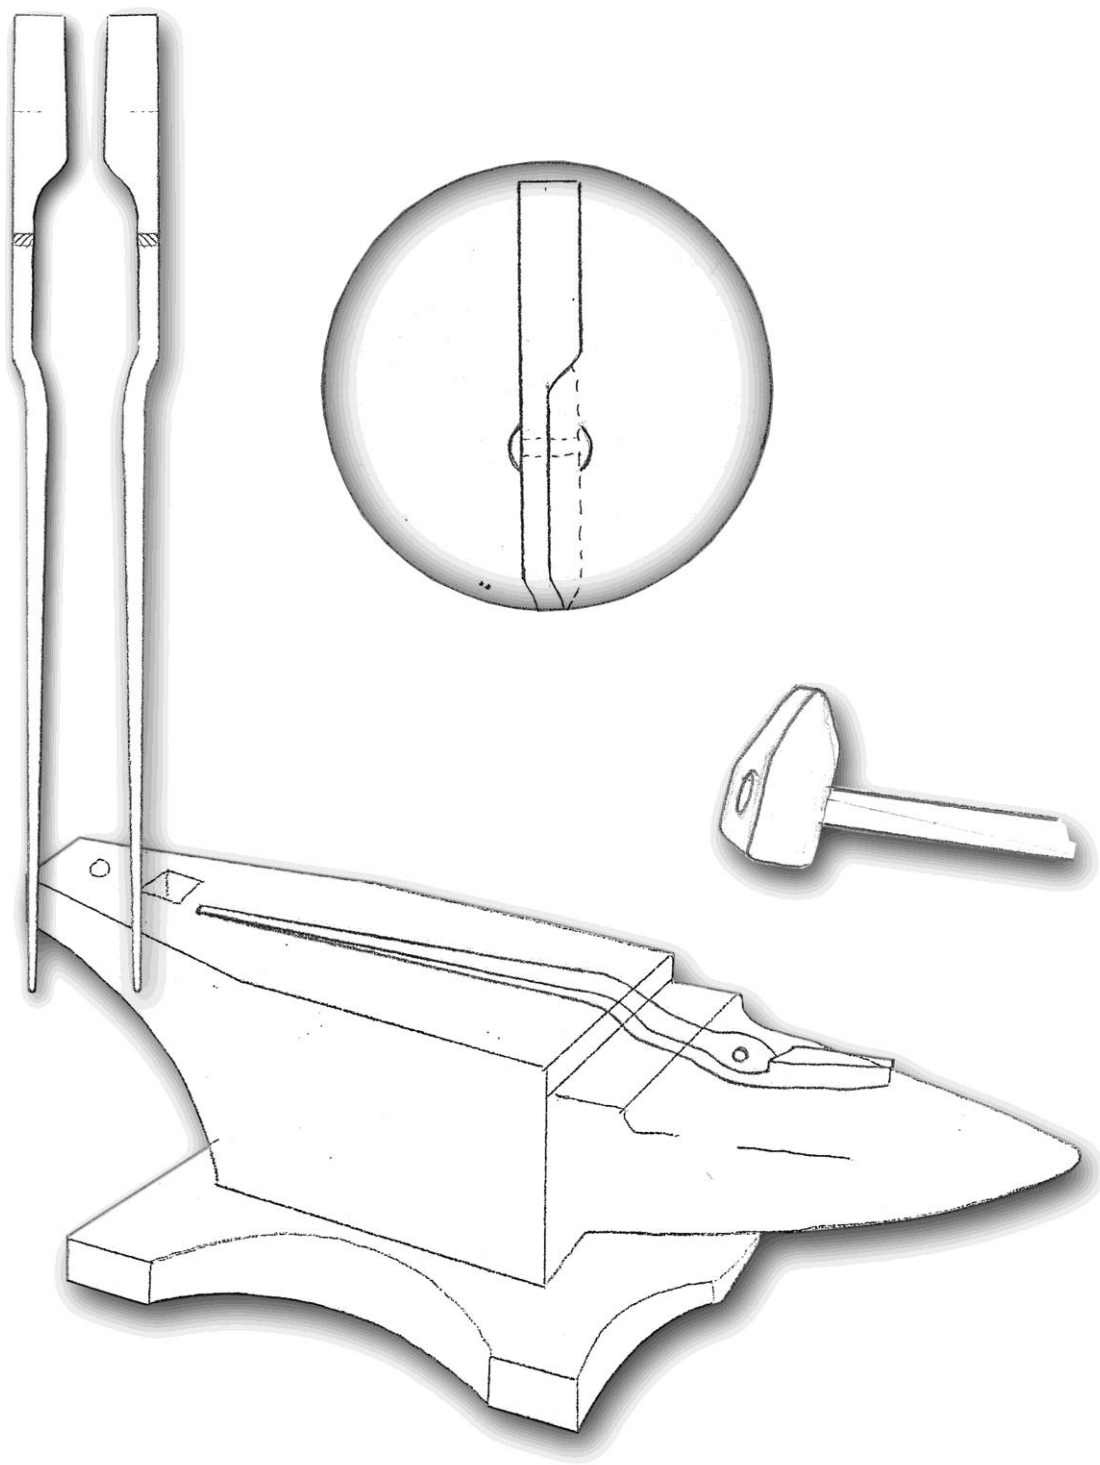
Формування ручки рицини (підгонка деталей)
